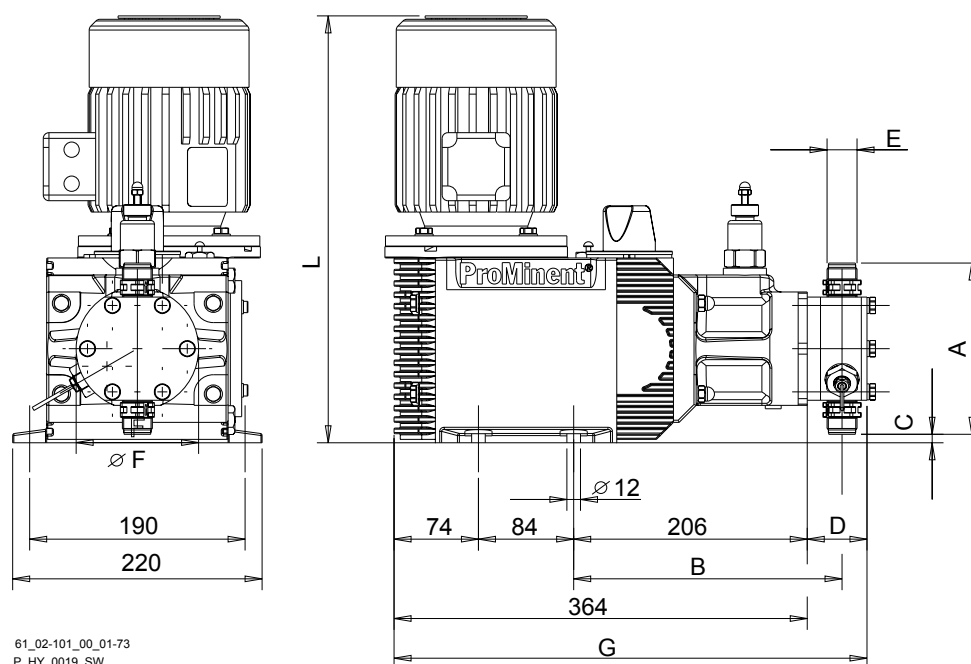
Hoja de dimensiones Hydro HP2 (HP2a H) - Dimensiones en mm
